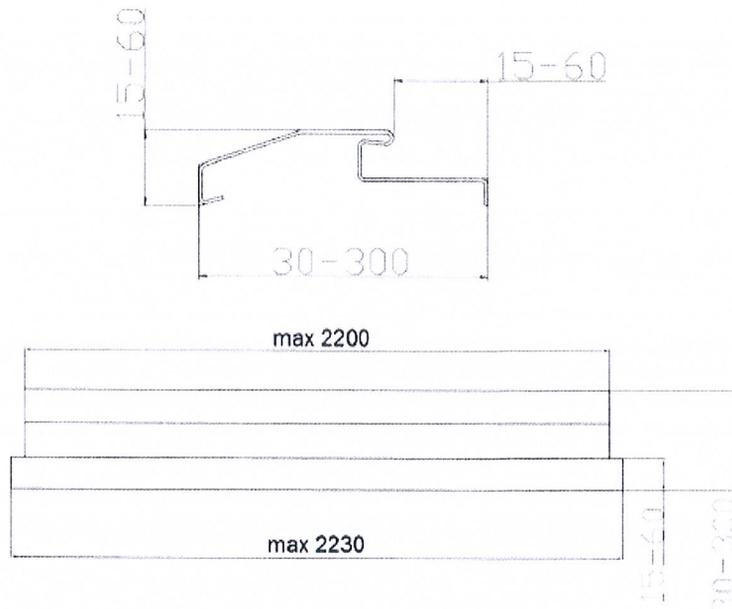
Befestigungsbleche für Schlösser im Alutürrahmen
